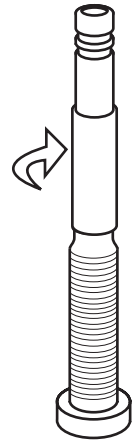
Die Verlängerung im Uhrzeigersinn auf das Ventil aufschrauben.
